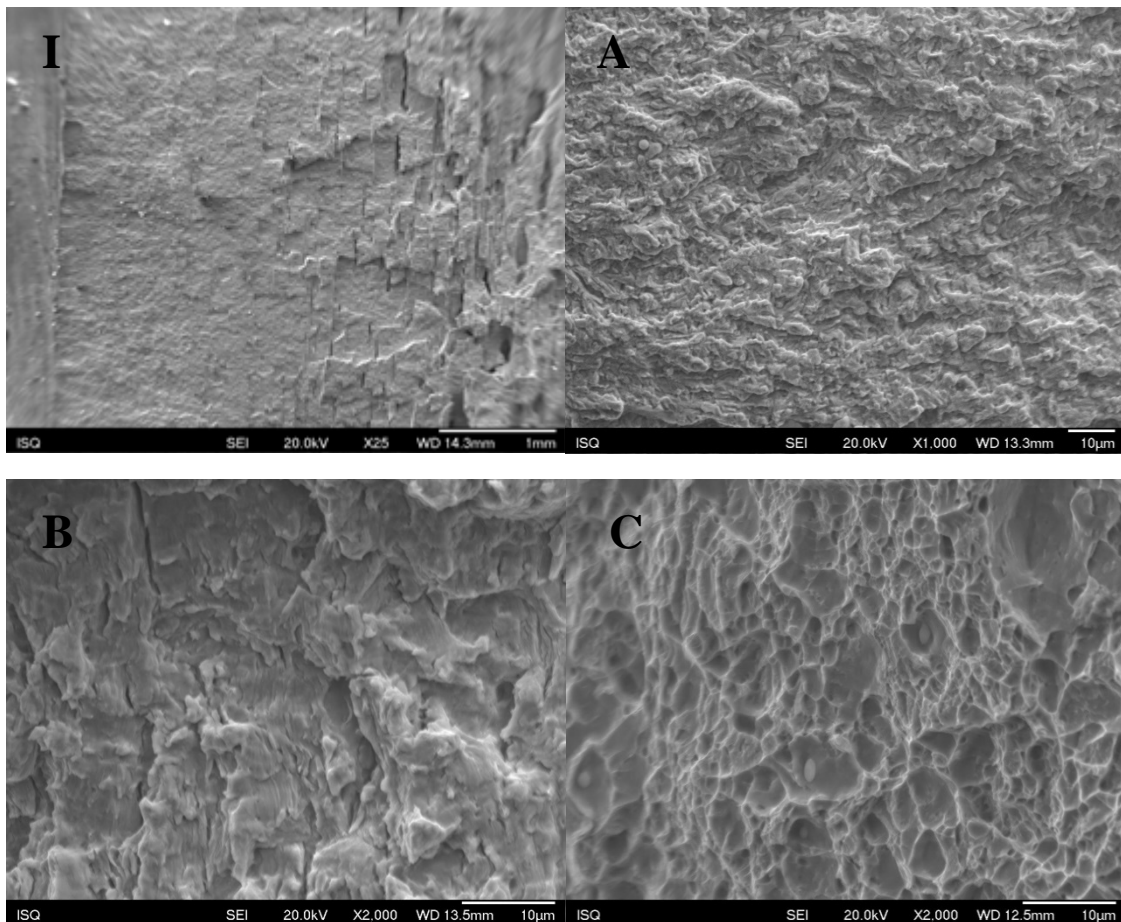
Ilustração da propagação da fissura do aço S 355 J2.
